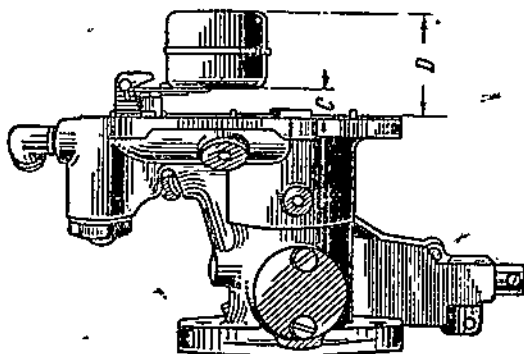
Проверка регулировки уровня топлива в поплавковой камере с подводом топлива через крышу
